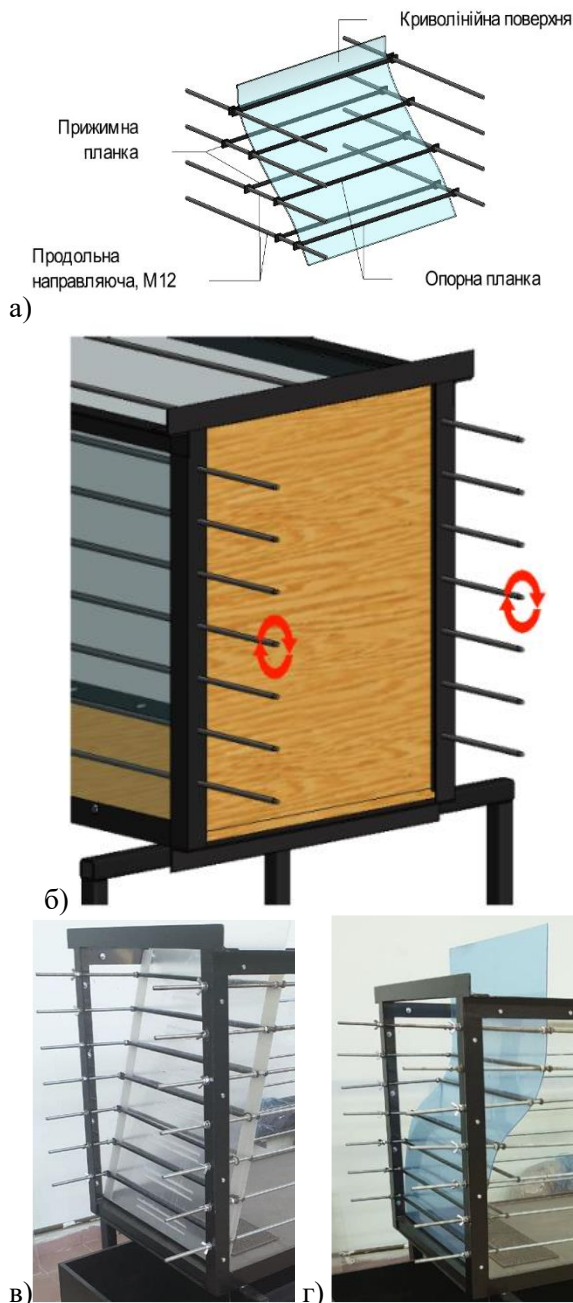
Формування криволінійної поверхні: а – схема механізму формування поверхні; б – пристрій пересування напрямних; в – плоска поверхня; г – криволінійна поверхня
